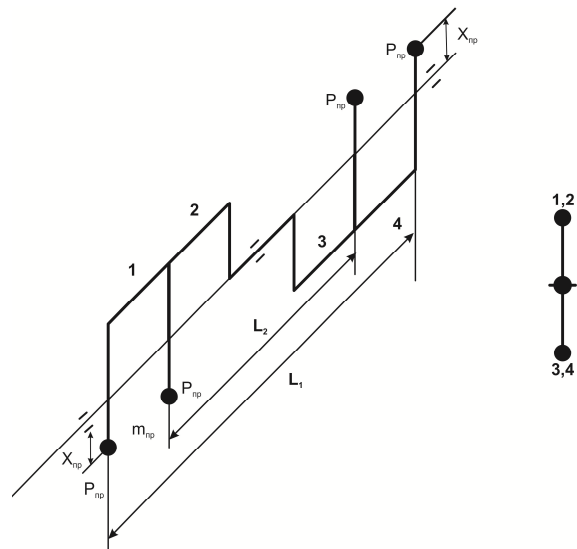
Схема коленчатого вала поршневого пневмодвигателя
